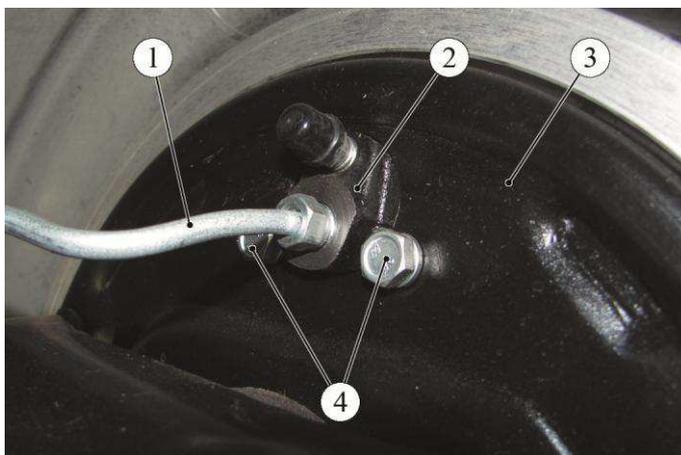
Снятие колесного цилиндра заднего тормоза:
